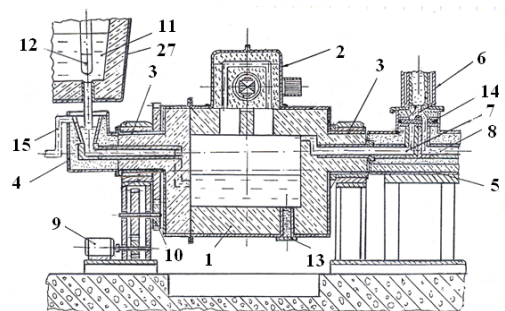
Конструкция двухковшовой литейной машины для изготовления полых биметаллических заготовок: 1 – металлоприемник; 2 – каналная печь;
